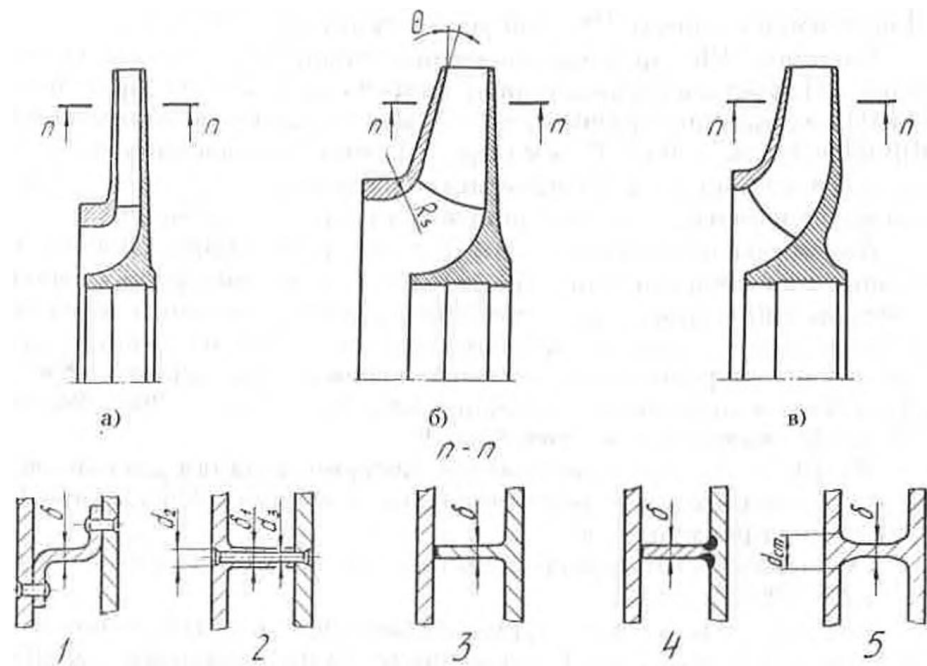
Конструктивные формы закрытых рабочих колес:
